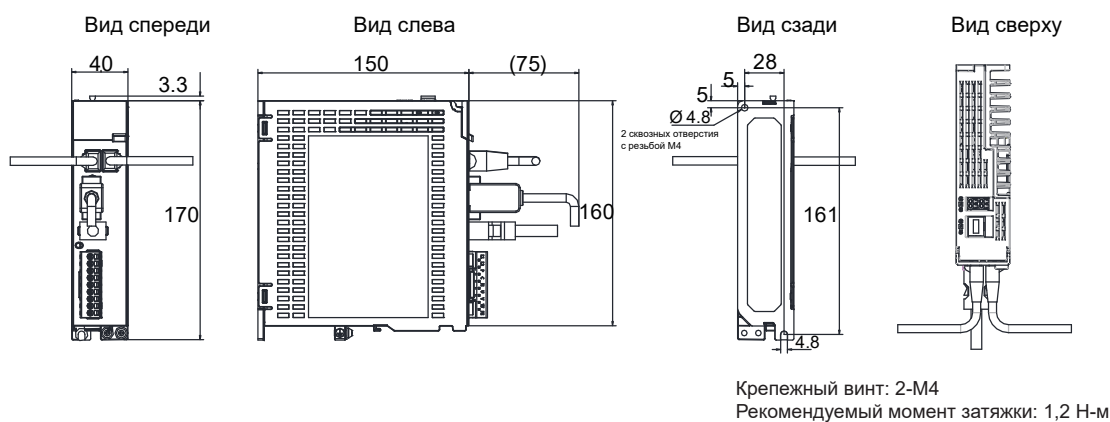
Габаритные размеры для типоразмера А (ед. изм: мм)
